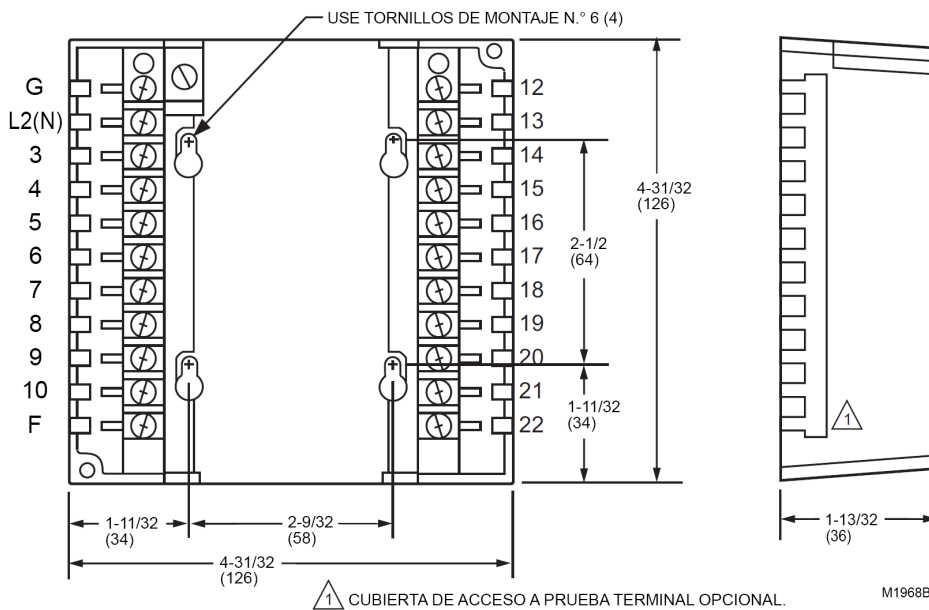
Vista superior y frontal de la subbase de cableado Q7800A1005 (2 caras) con dimensiones en pulgadas (mm).
